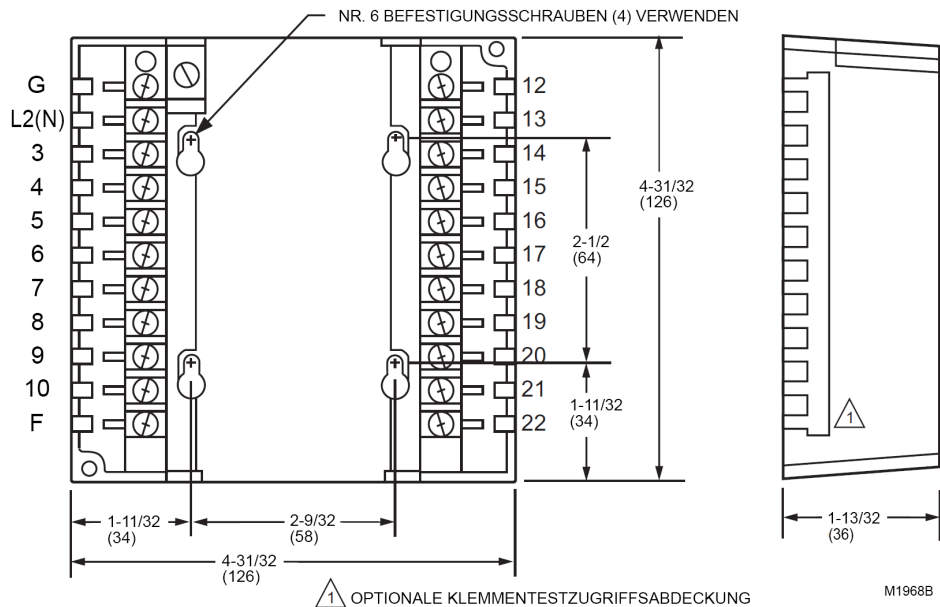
Draufsicht und Frontansicht des Q7800A1005-Verdrahtungssockels (2-seitig) mit Abmessungen in Zoll (mm).
